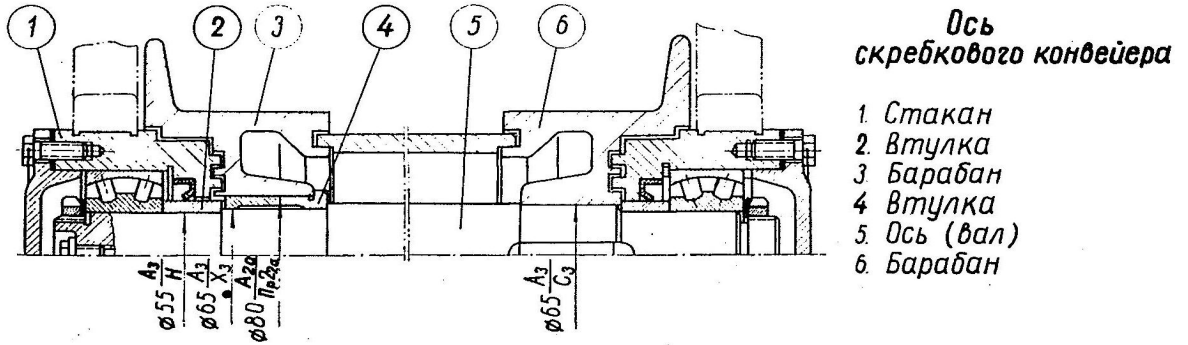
Розташування на валу скребкового конвеєра втулки, що фіксує положення радіального роликового сферичного підшипника
